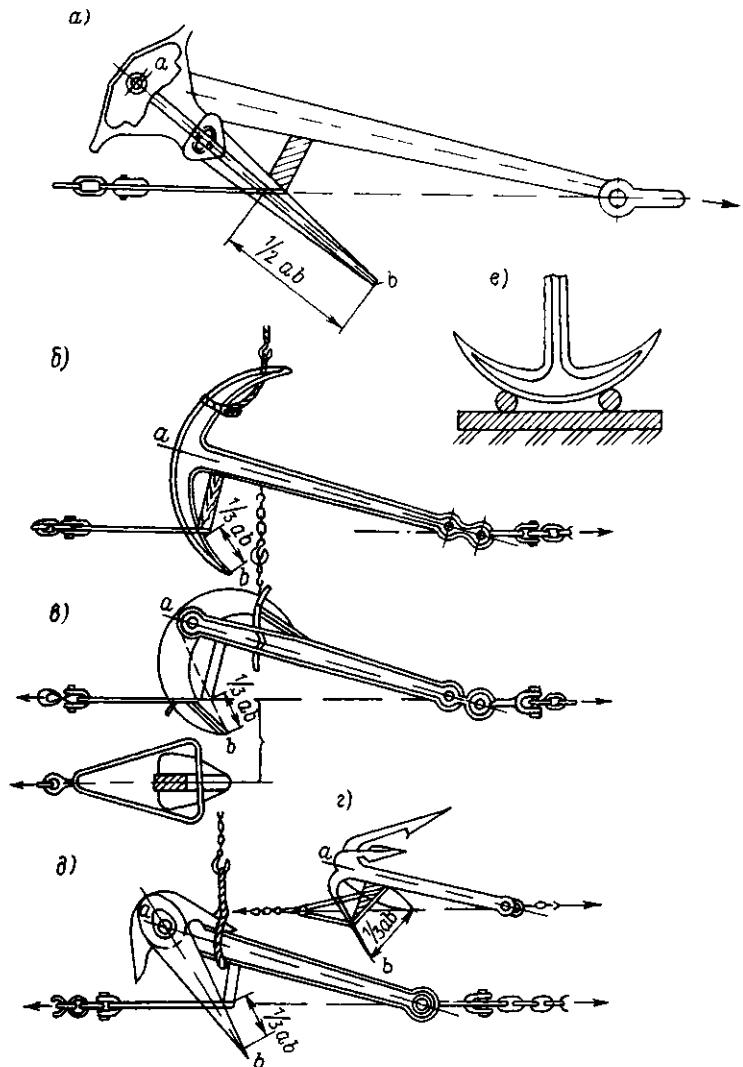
Испытания якорей на прочность: растяжением – а – катерный якорь; б – адмиралтейский якорь; в – якорь Тротмана; г – якорь без штока; д – якорь Холла; бросанием – е – адмиралтейский якорь
